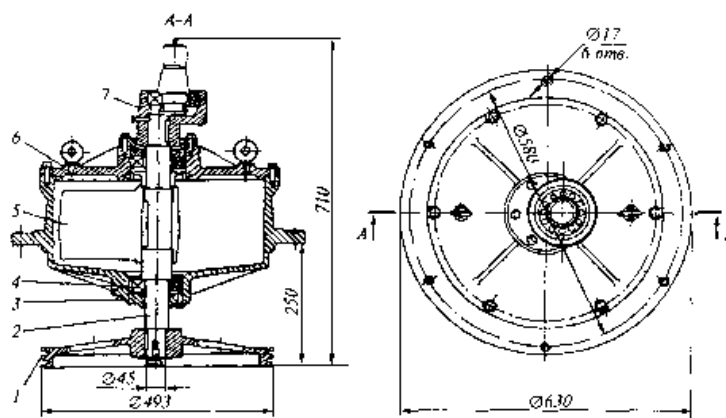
Эксцентриковый колебатель привода просеивателя А1-КСБ
